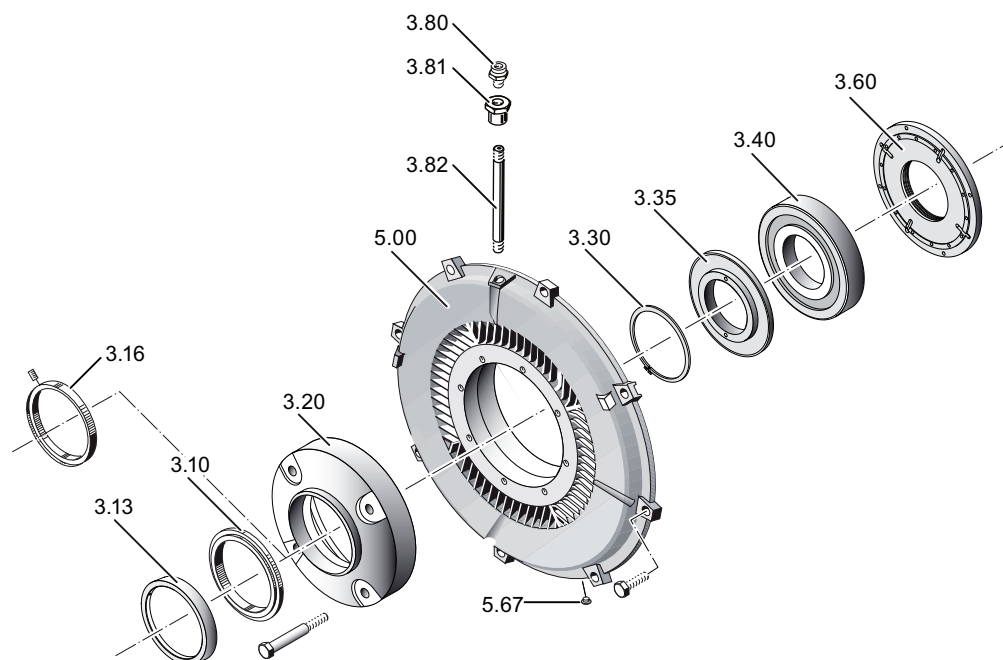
Подшипник качения, приводная сторона (DE) без корпуса подшипника
